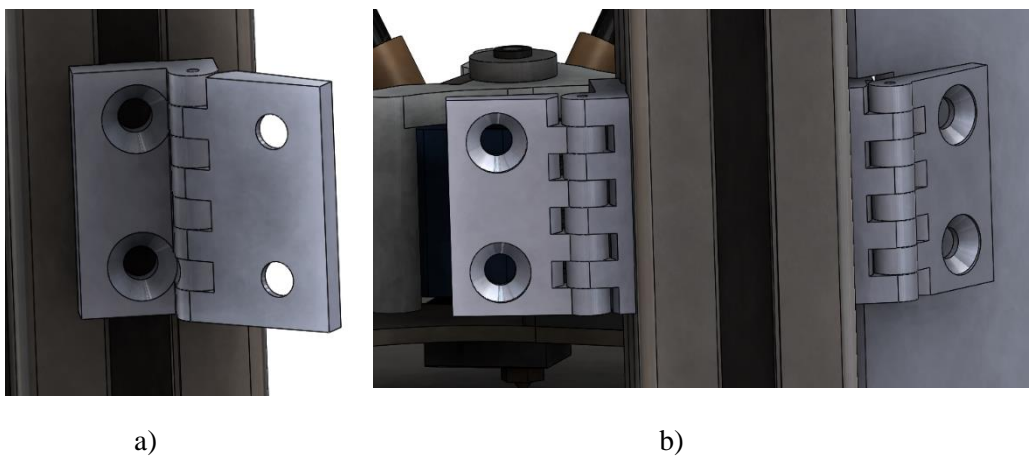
a) pormenor da dobradiça; b) pormenor da montagem das dobradiças
